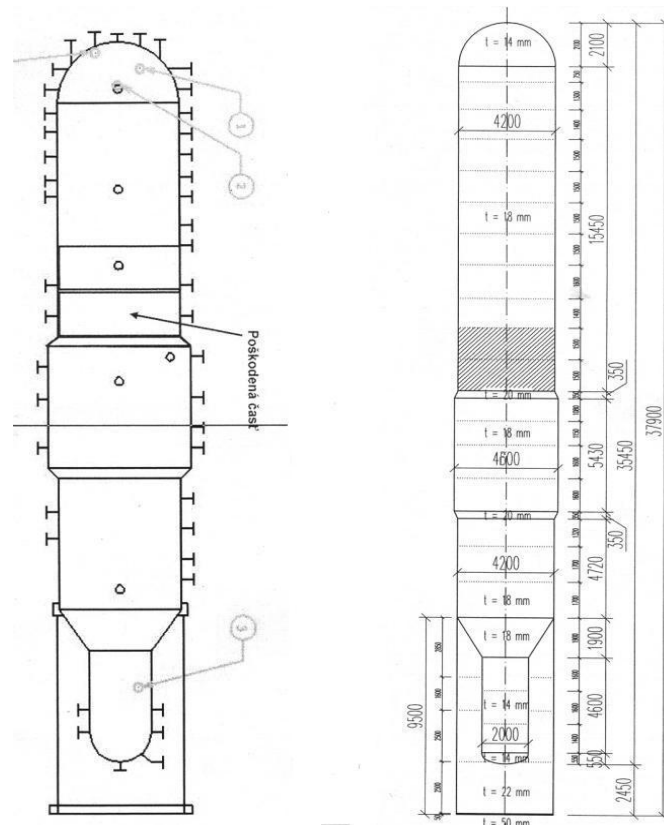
Rozsah lokálneho vydutia steny a detailný záber na poruchu
